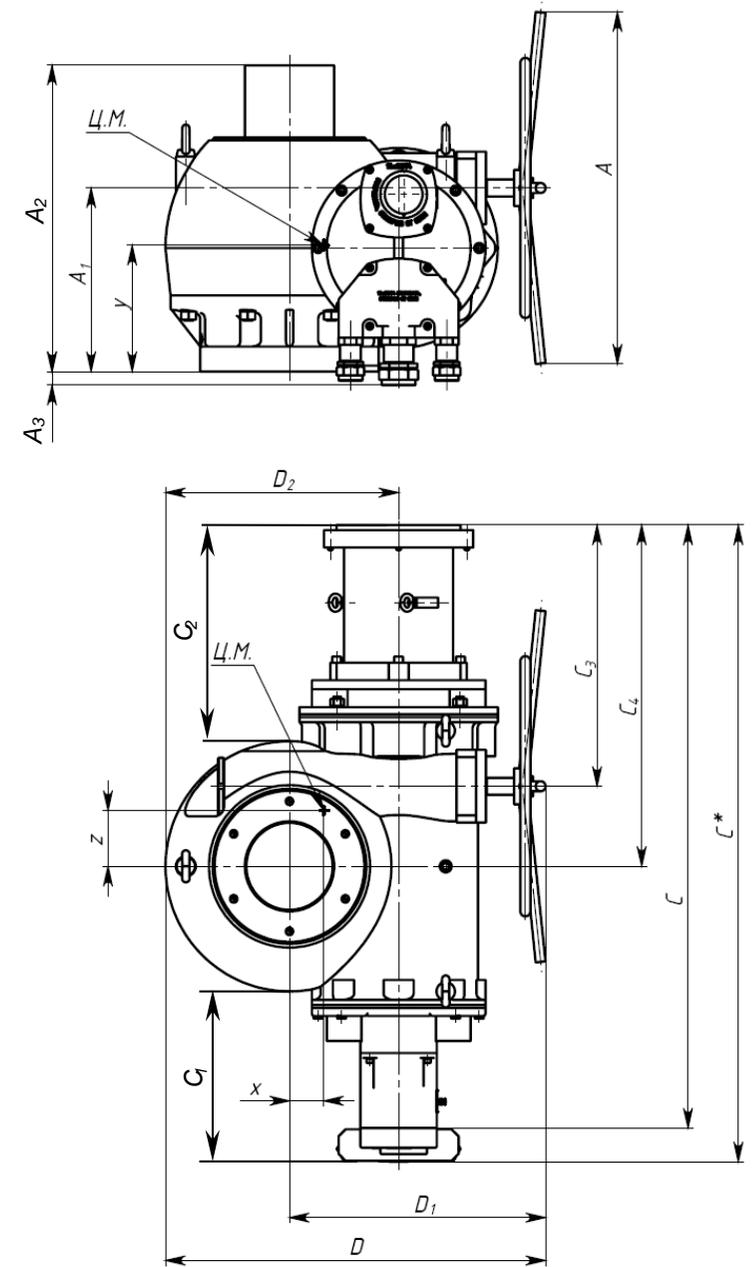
е – Габаритные размеры привода конструктивной схемы 44
